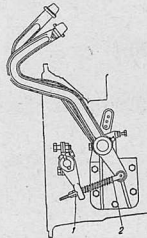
Привод механизма сцепления автомобиля ЗИС-5
